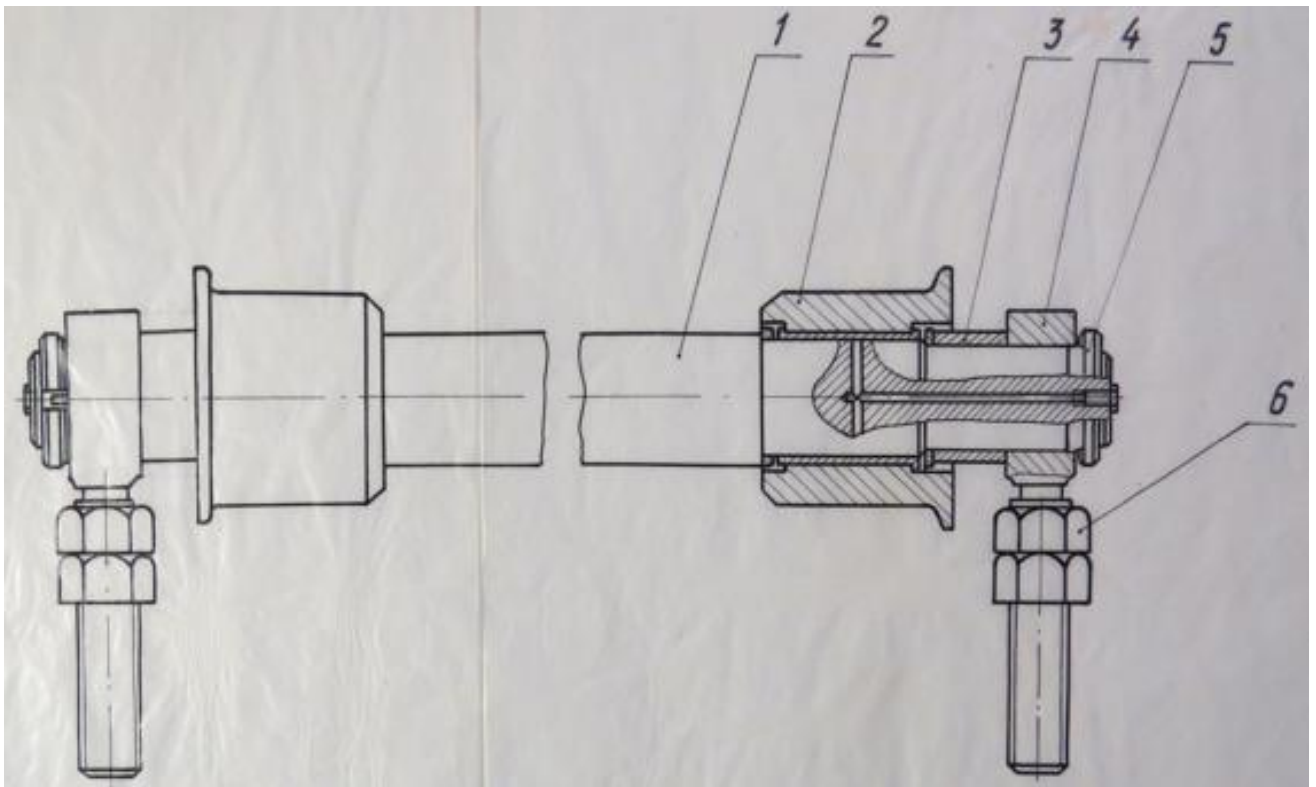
Натяжний пристрій скребкового ланцюга:
